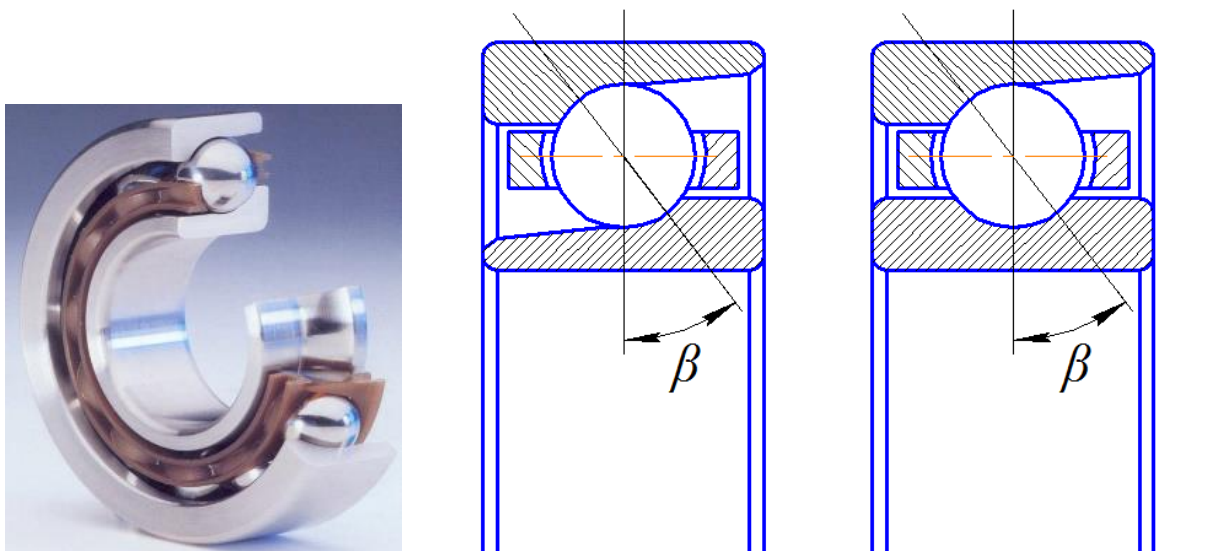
Конструкція кульового радіально-упорного підшипника
